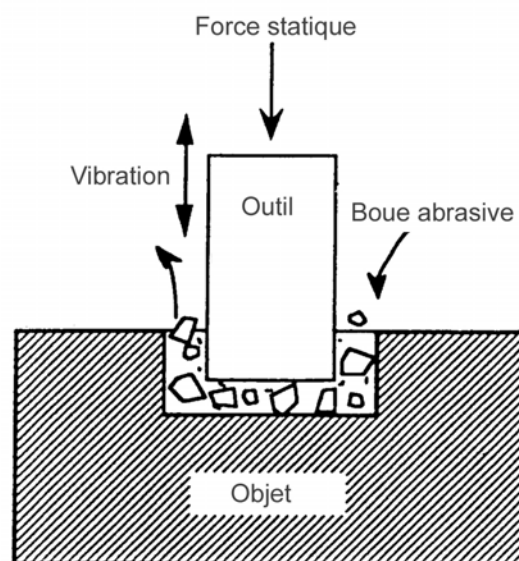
Principe de l'usinage ultrasonique USM.
